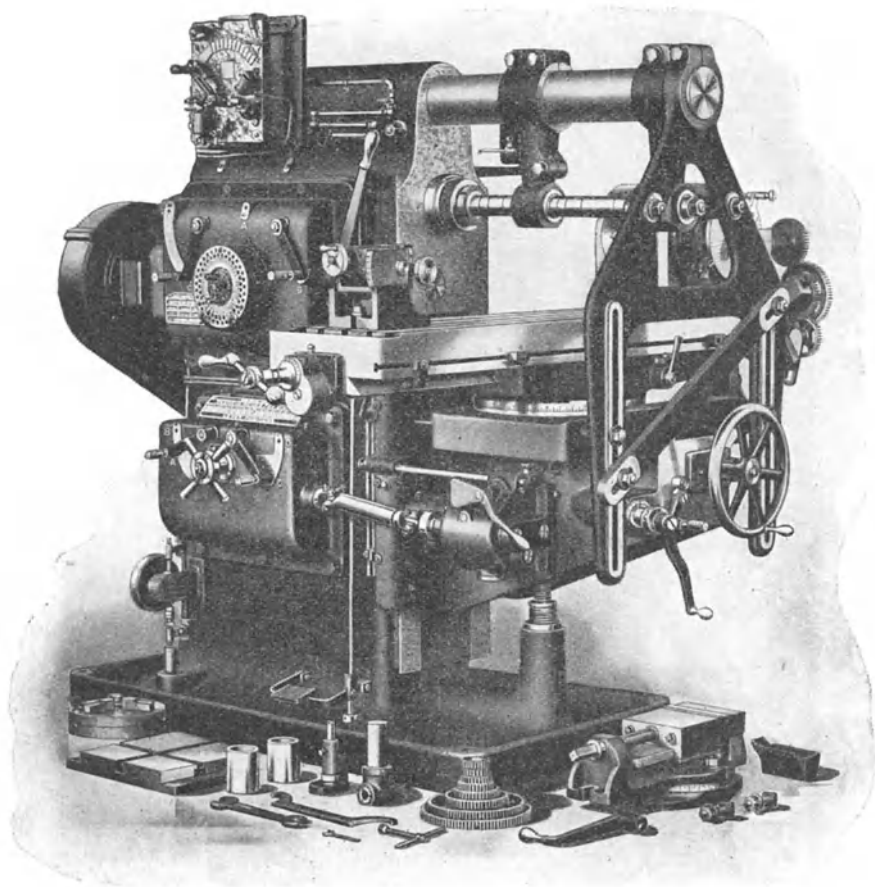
Die Universalfräsmaschine der Cincinnati-Co.
